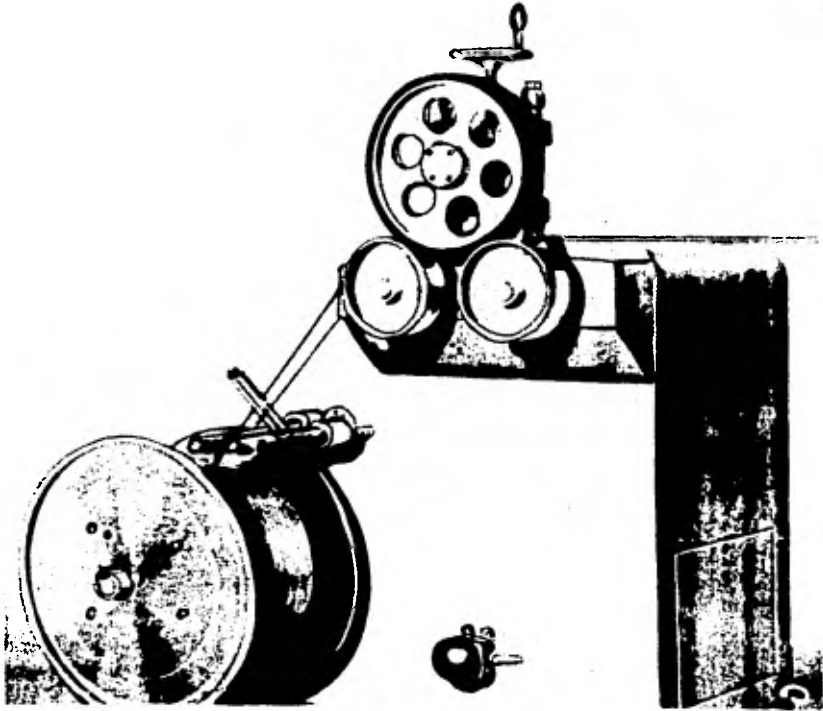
COMBINACION DE JALADOR Y ENROLLADOR DE ALAMBRE PARA TAMBORES (DE ENROLLADO) CON 60 CM. DE DIAMETRO MAXIMO.
